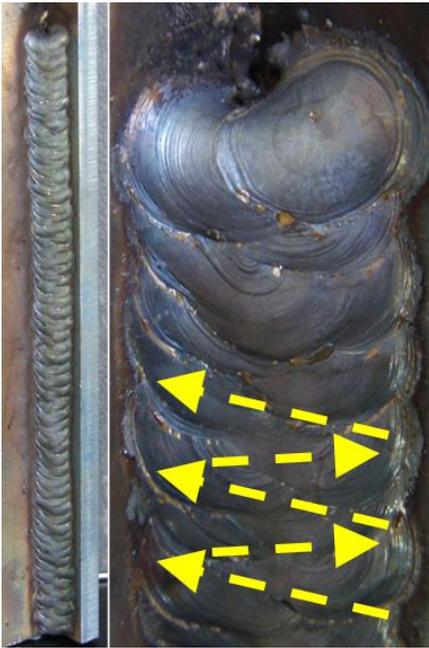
Fehlerhafte Steignachtschweißung durch ungünstige Elektrodenführung (Stahl 8mm, M21, 1mm G3Si1)
